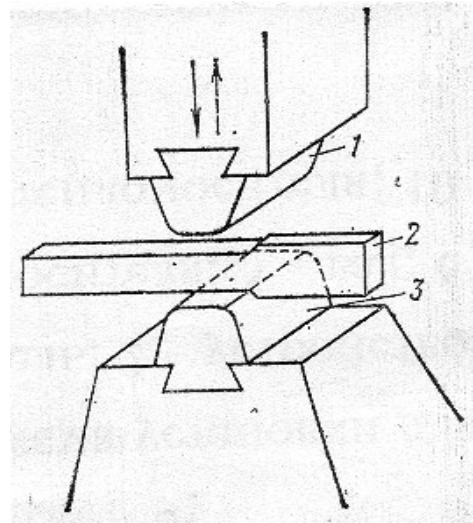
Схема процесу вільної ковки: 1 – верхній бойок; 2 – заготовка; 3 – нижній бойок.
